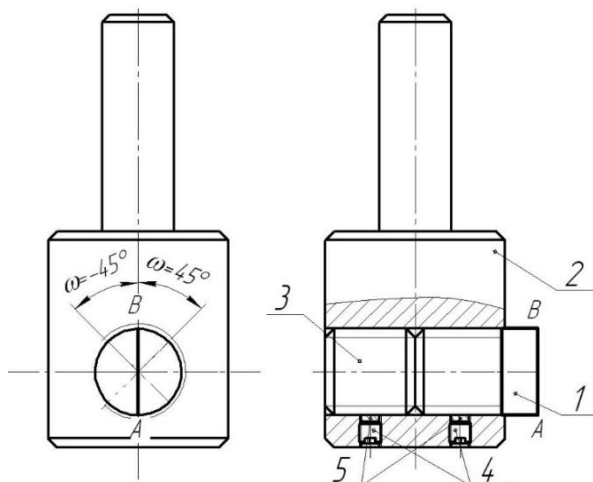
Конструкція експериментальної кінцевої циліндричної фрези з можливістю зміни кута нахилу винтової режущої кромки АВ - ω
